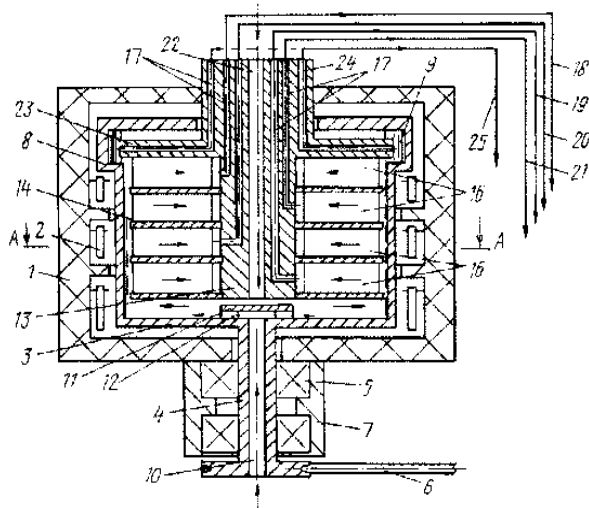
Продольный разрез установки: 1 - теплоизоляционного корпуса; 2 - кольцевыми нагревателями 2; 3 – ротор; 4- валу; 5- подшипники; 6 - приводом; 7 - втулка 7; 8 - кольцевая камера; 9 - тяжелой фракции; 10 - центральный осевой канал; 11 - шайба; 12 - радиальные каналы; 13 - неподвижный ротор; 14 - диски; 15 - лопатками; 16 - технологические камеры; 17 - осевых каналов 17; 18, 19, 20, 21 - трубопроводы; 22 - канал для подачи исходного продукта; 23 - напорный диск; 24 - каналы напорного диска; 25 - трубопроводы.
